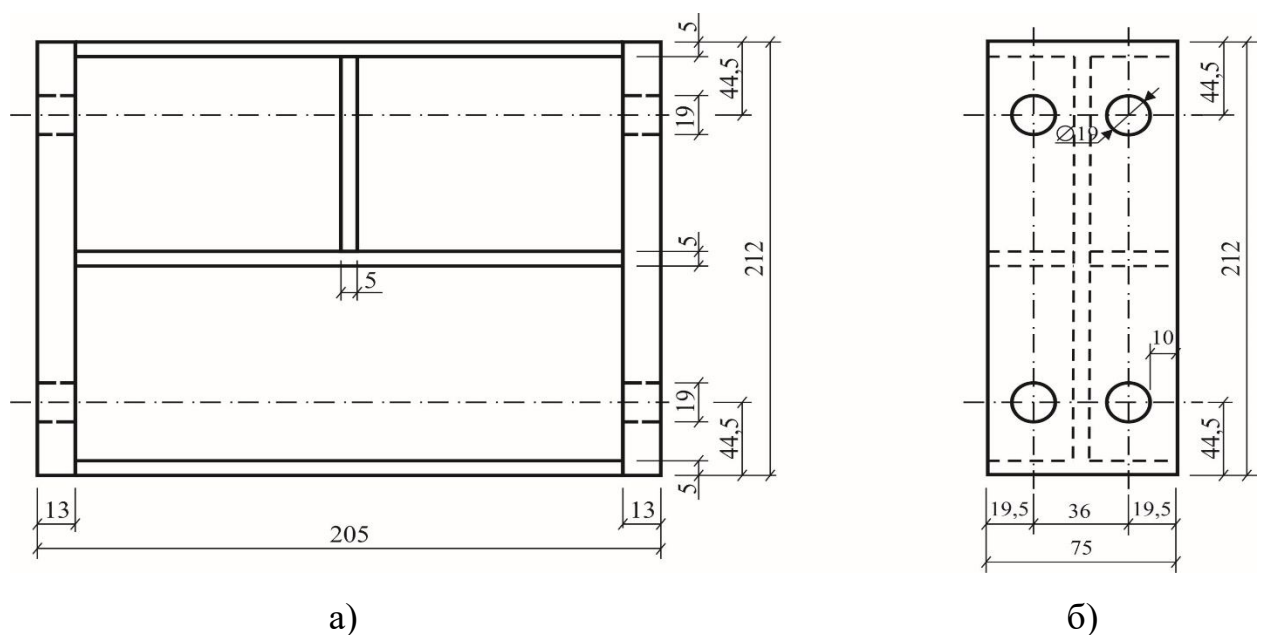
Конструкція металевої вставки: а) фронтальний вид; б) вид збоку
